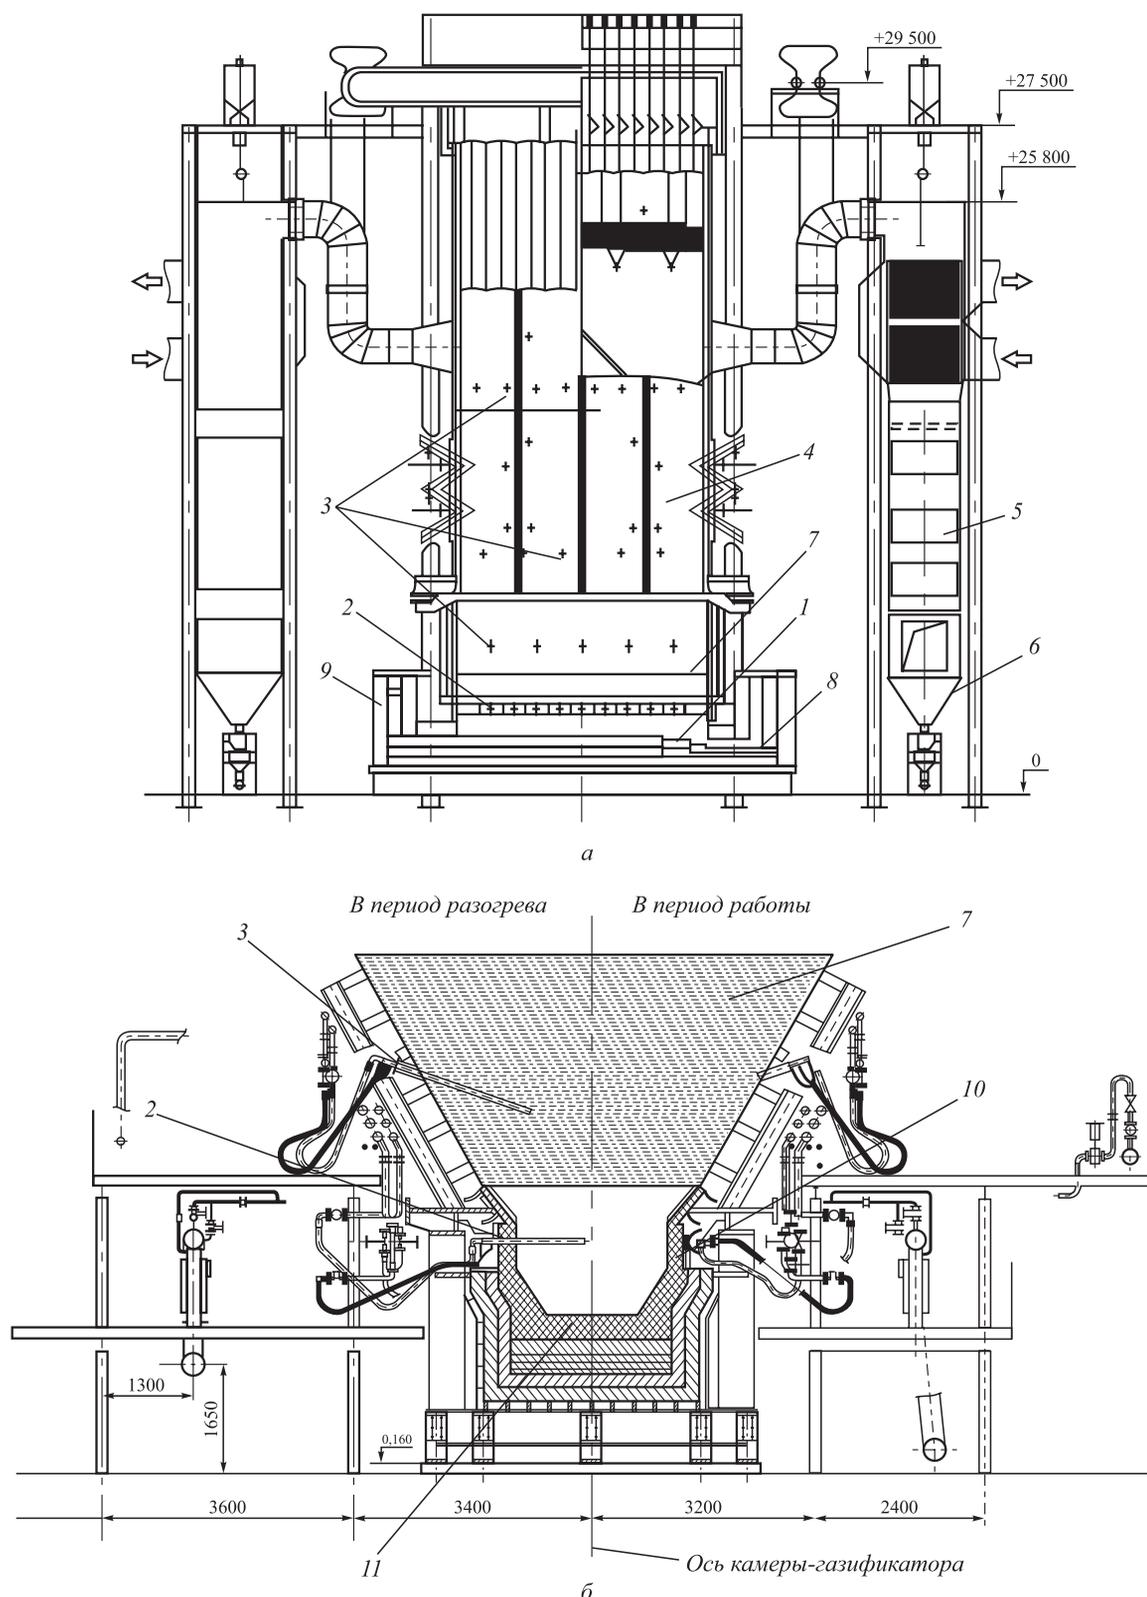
Общий вид установки (а) и камера сжигания угля (б) в шлаковом расплаве [9]:
